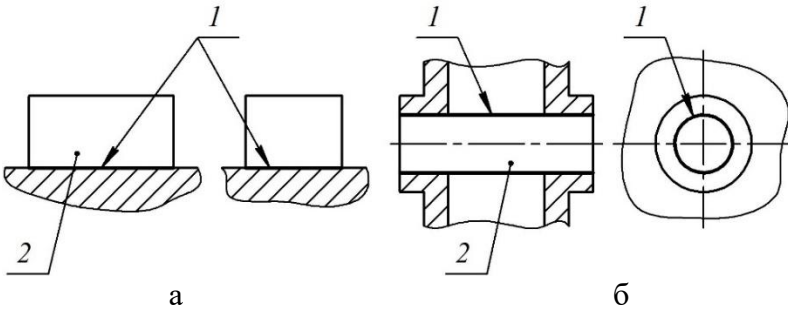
База: 1 – базувальна поверхня, 2 – деталь
